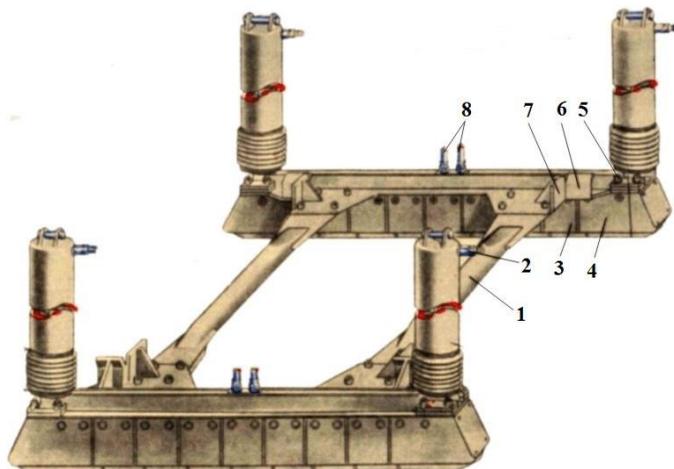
Общий вид магнитно-рельсового тормоза:
